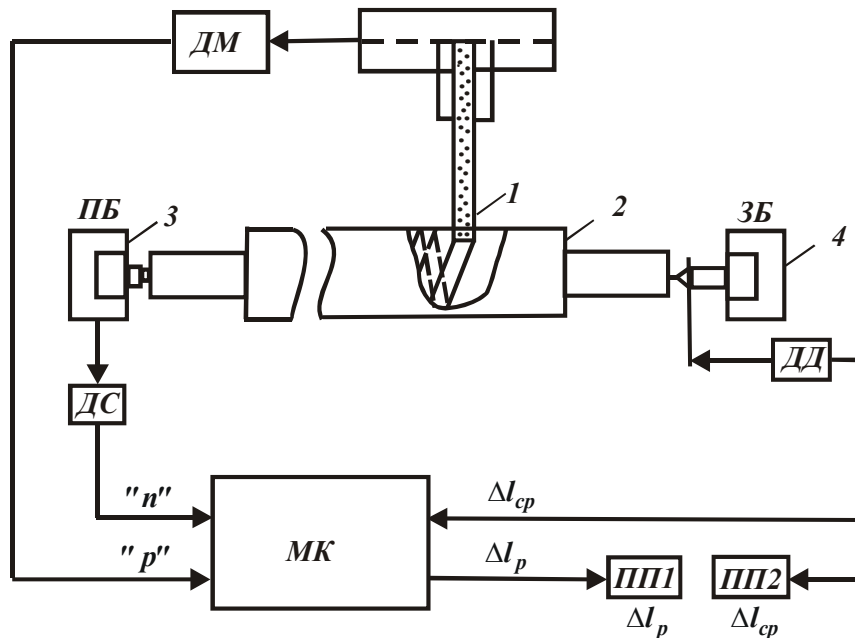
Система компьютерной диагностики процесса резбошлифования: 1 - шлифовальный круг; 2 - заготовка; 3, 4 - передняя и задняя бабки резбошлифовального станка; ДМ - датчик мощности шлифования; ДС - датчик скорости детали (частоты вращения заготовки); ДД - датчик деформации; МК - микроконтроллер.
